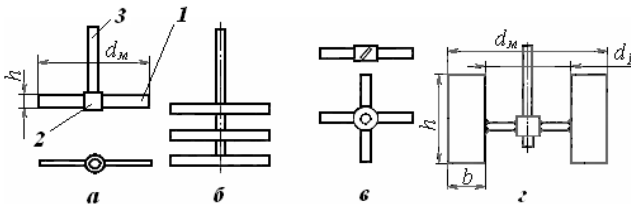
Конструкції лопатевих мішалок: а – дволопатєва; б – багаторядні; в – багатолопатєві; г – з вертикальними лопатями
